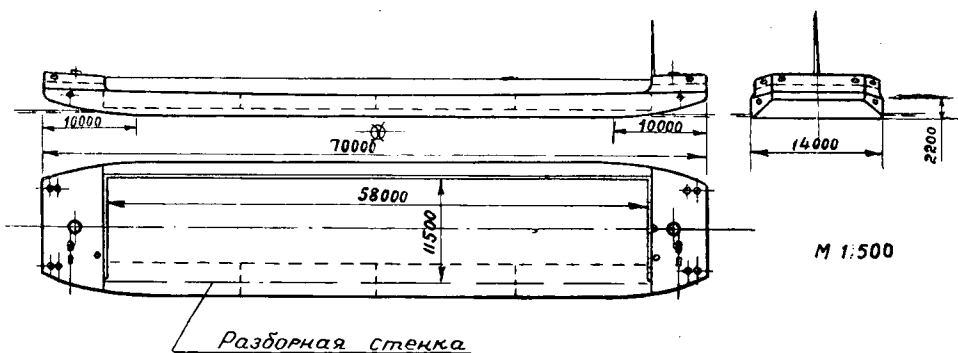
Общий вид открытой палубной металлической баржи с крен-балластными цистернами.
